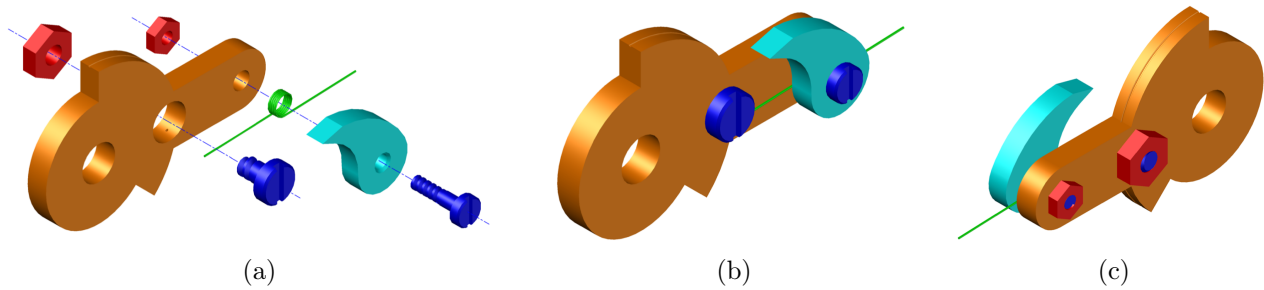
a) Distribución de piezas, b) Perspectiva derecha y c) Perspectiva izquierda del ensamblado de la palanca con horse head
